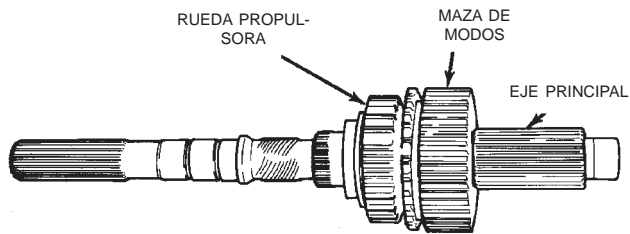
Instalación del conjunto de horquilla y maza de posiciones
